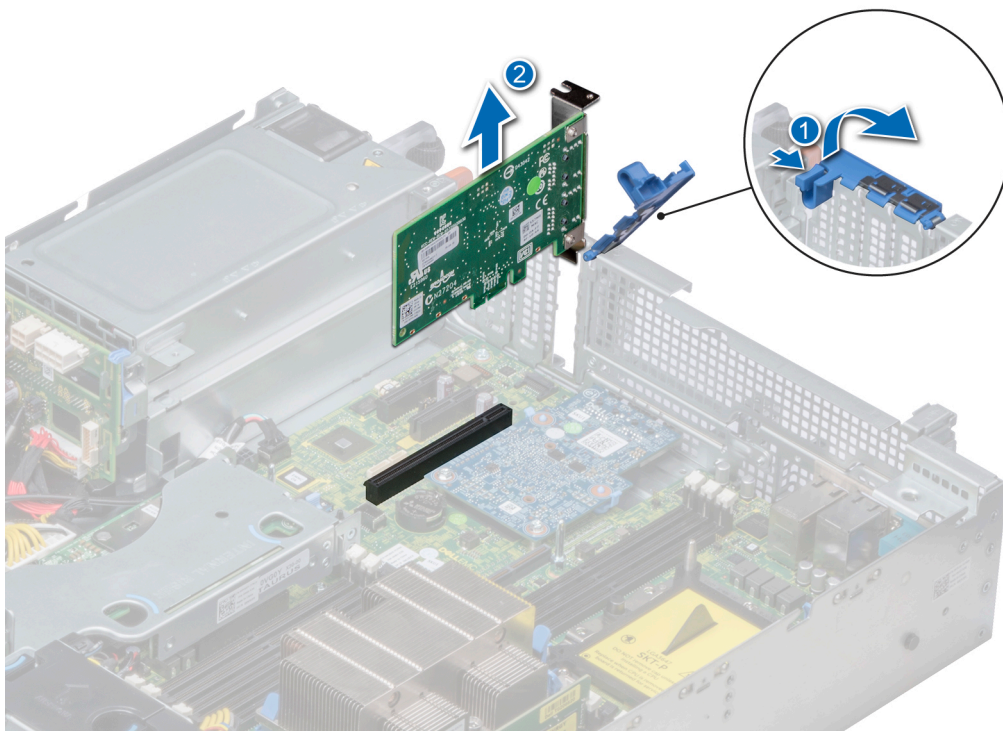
Desmontaje de una tarjeta de expansión de la placa base
